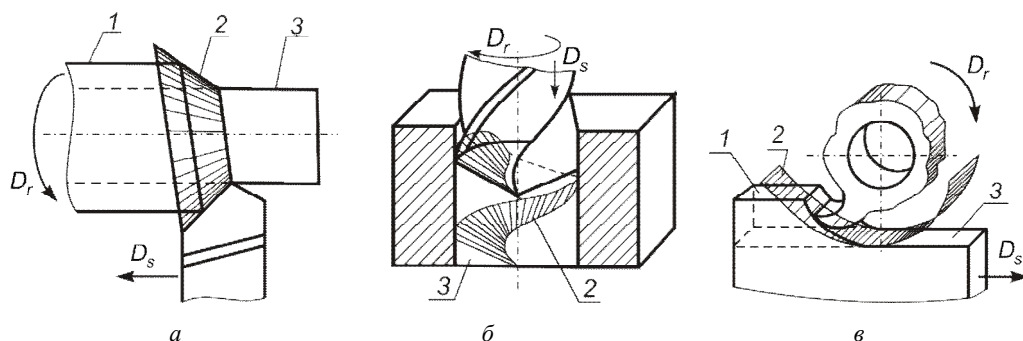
Поверхности при точении (а), сверлении (б) и цилиндрическом фрезеровании (в):
